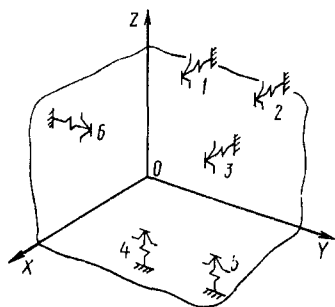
Схема базирования корпуса шпиндельного узла вертикально-фрезерного станка
